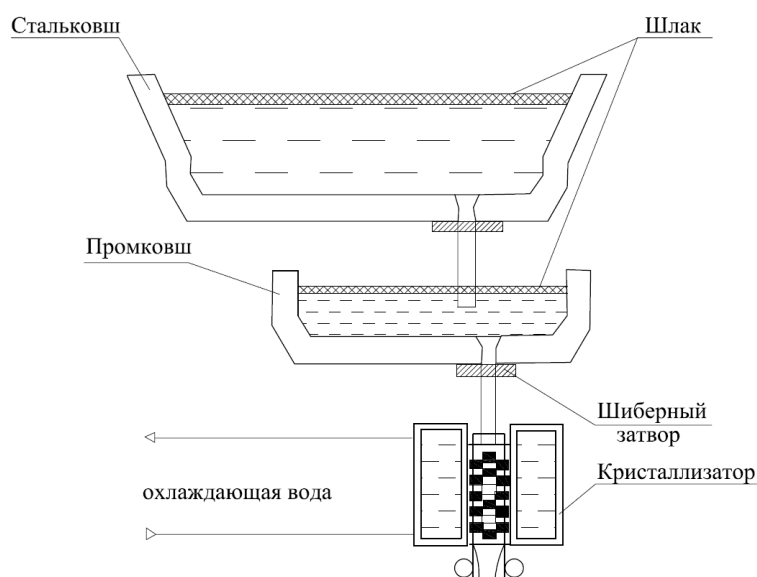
Схема выпуска металла из кристаллизатора на МНЛЗ
